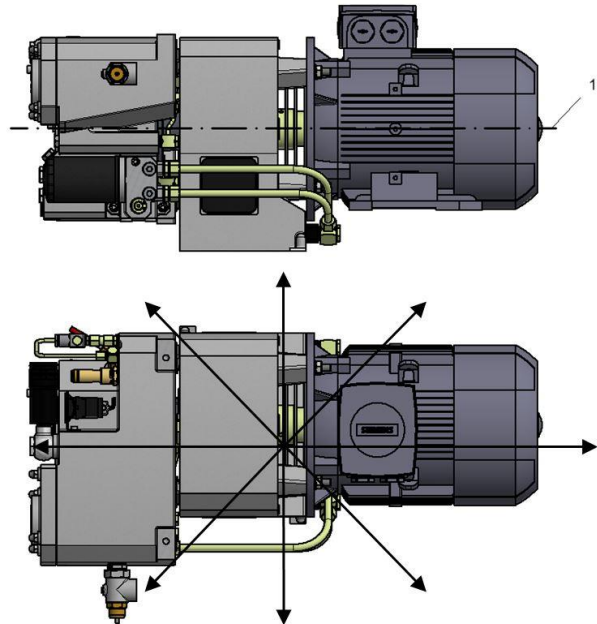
beliebige Einbaulage bei horizontale Kompressorachse
